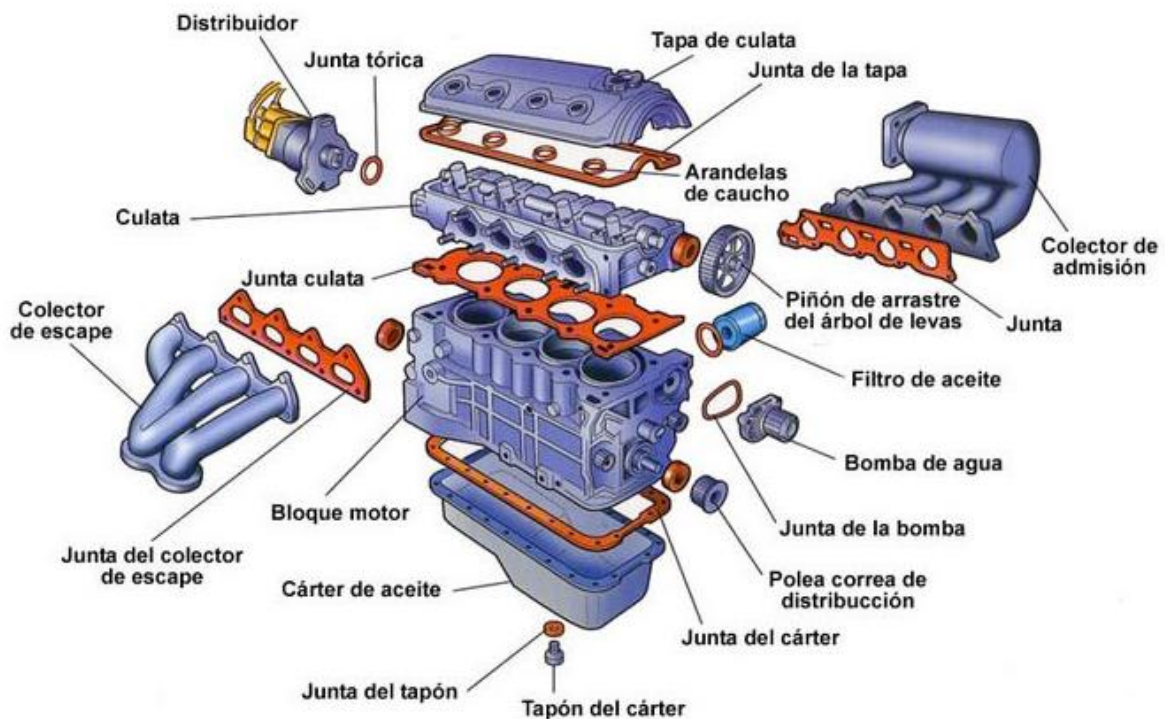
Despiece de un motor a combustión interna de 4 cilindros en línea.
